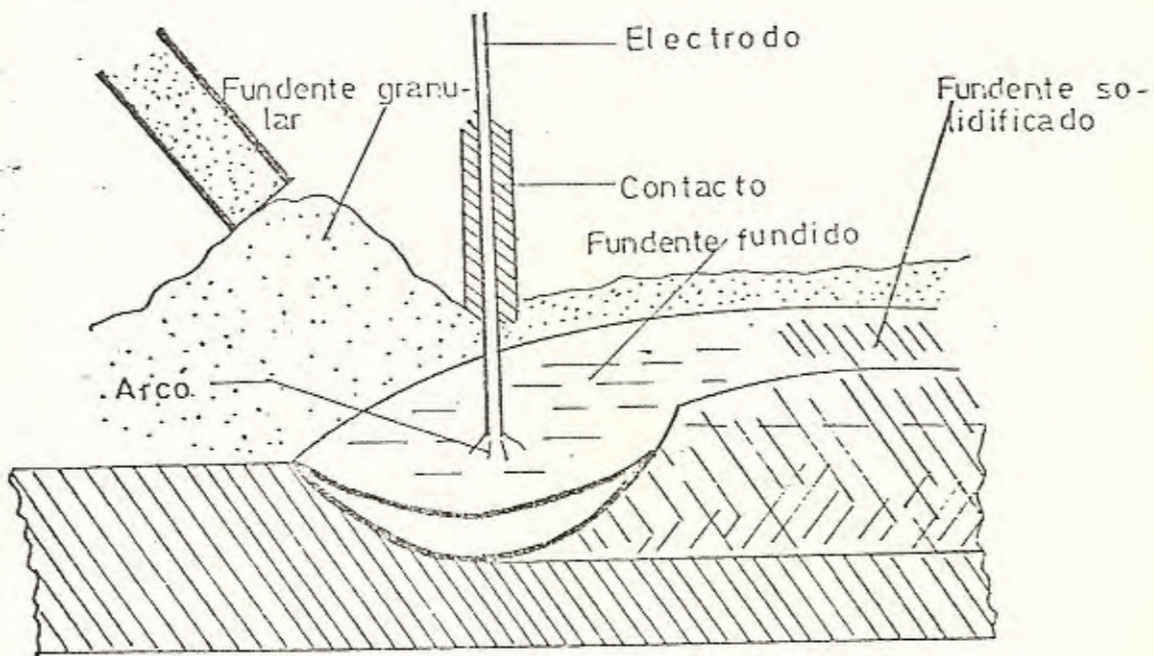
PROCESO DE SOLDADURA AL ARCO SUMERGIDO
